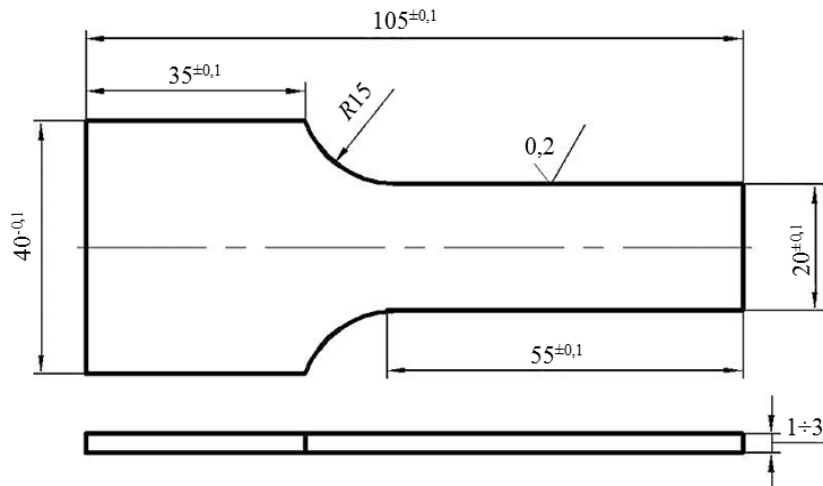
Образец для виброиспытаний по первой изгибной форме
